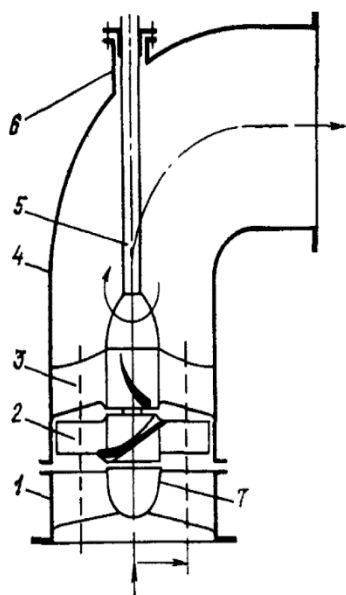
Компоновочная схема и конструкция осевого насоса: 1 – приемный патрубок; 2 – рабочее колесо; 3 – спрямляющий аппарат (лопаточный отвод); 4 – корпус; 5 – вал; 6 – сальник; 7 – обтекатель
